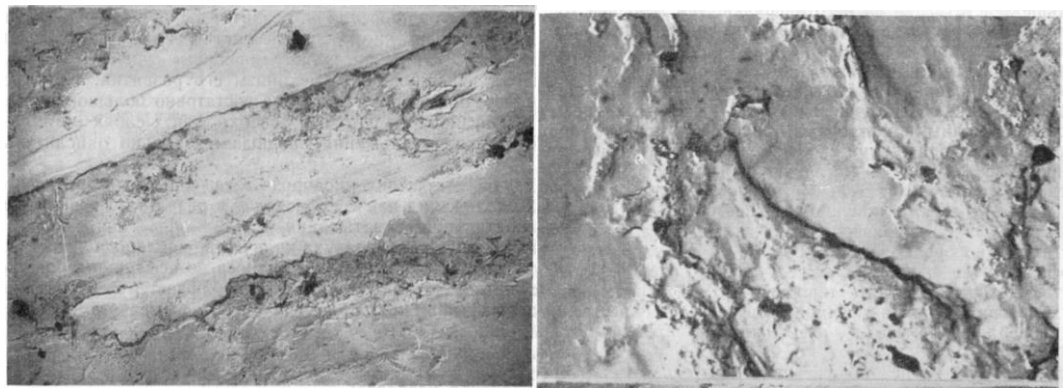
Абразивний знос робочої поверхні плунжера
